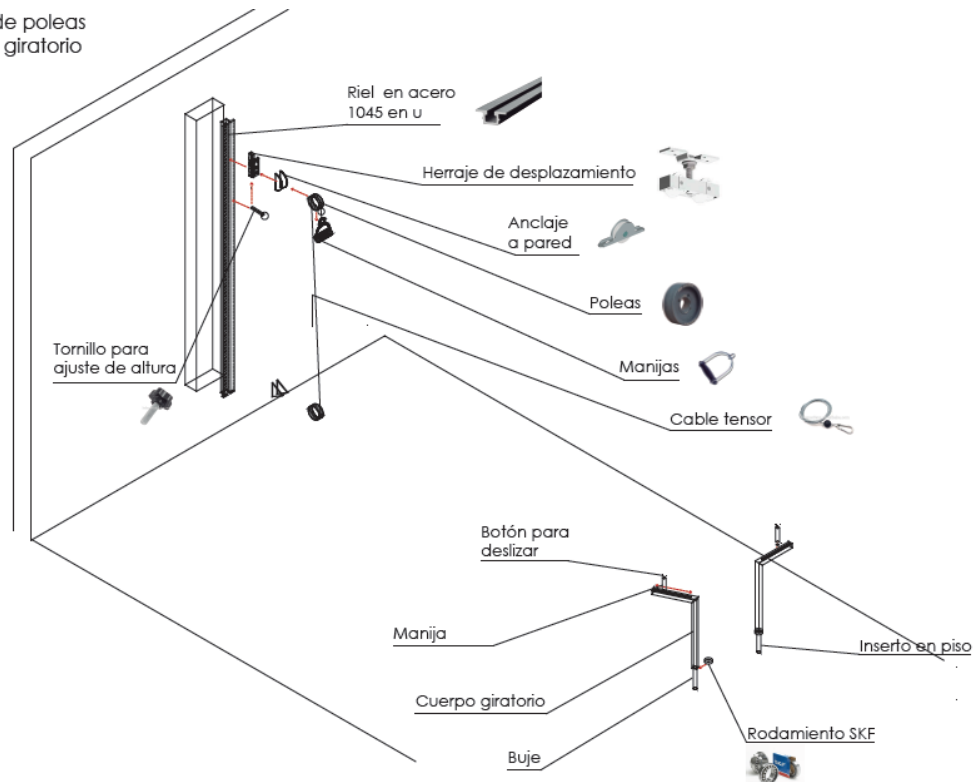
Detalle constructivo Sistema giratorio y de poleas. Autoría propia.
